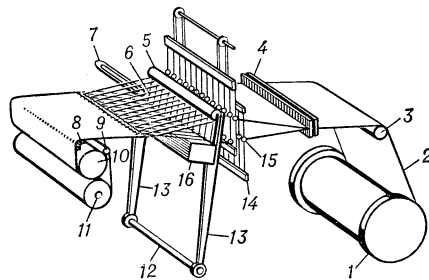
Принципиальная схема образования ткани на ткацком станке: 1 — навои; 2 — нити основы; 3 — скало; 4 — ламели; 5 — верхний; 6 — бёрдо; 7 — челнок; 8 — грудница; 9 — направляющий вал; 10 — вальня; 11 — товарный вал; 12 — подбатанный вал; 13 — лопасть батана; 14 — ремизка; 15 — глазок галева; 16 — батан.
